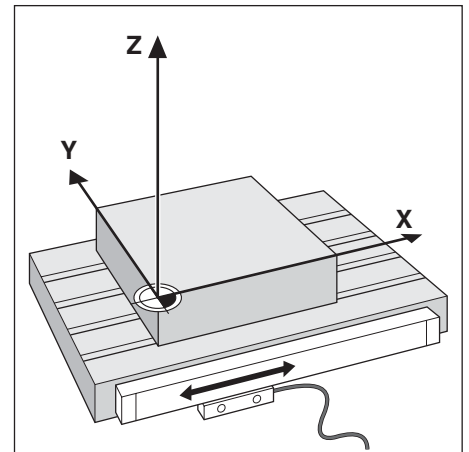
Wegmeßsystem für eine Linearachse, z.B. für die X-Achse
